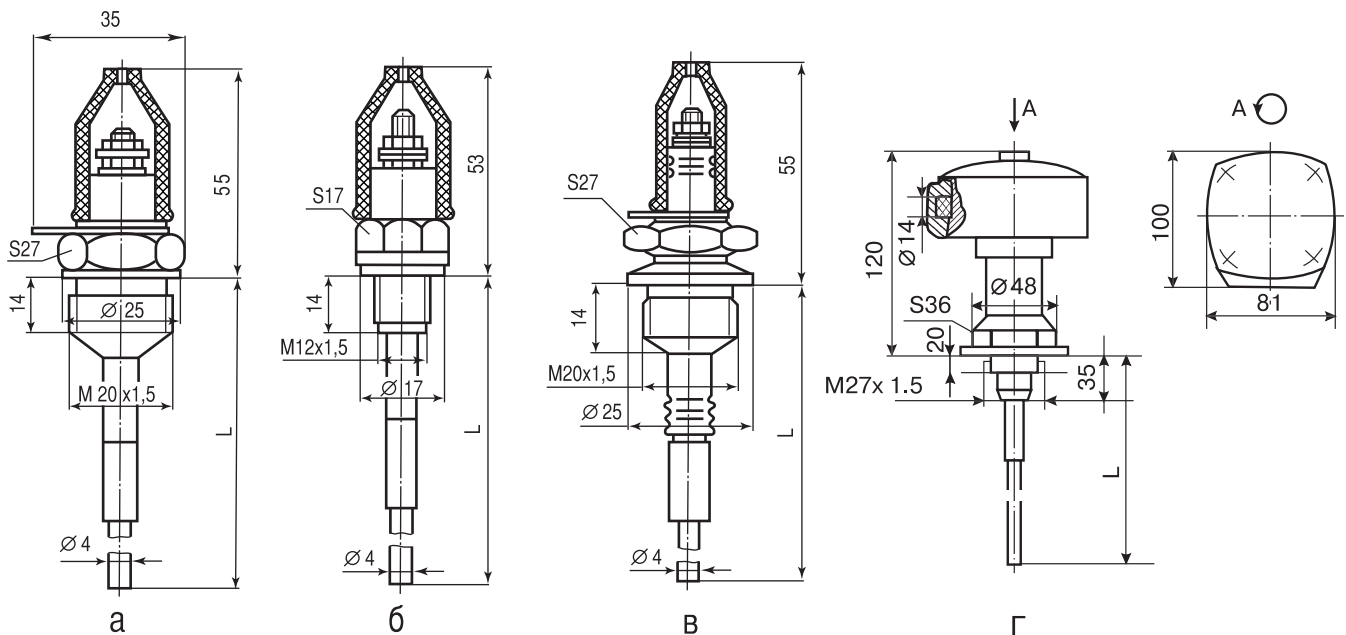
Общий вид, габаритные и установочные размеры датчиков.
